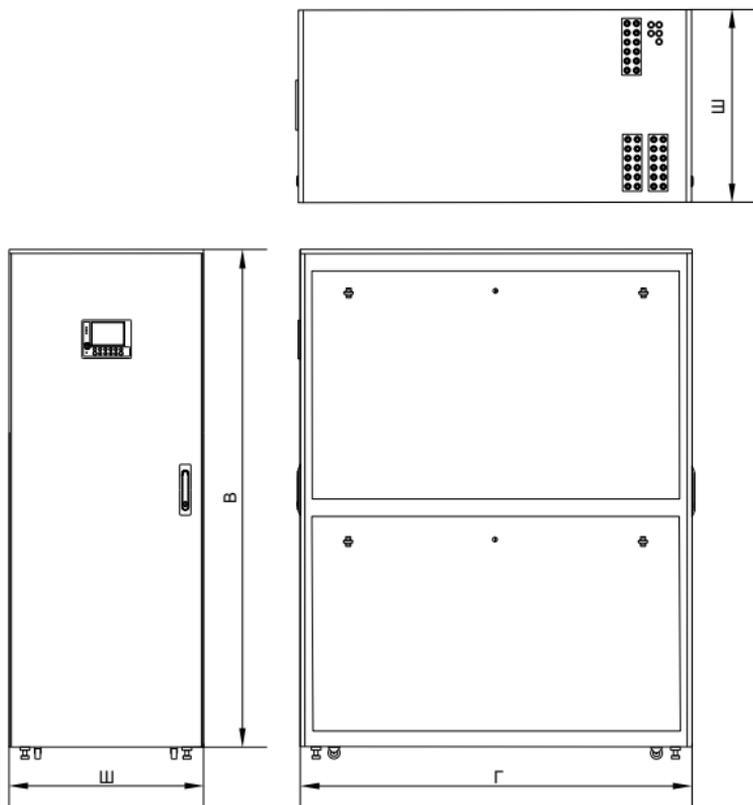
Габаритные размеры аппаратного шкафа КСОД серии DCI
